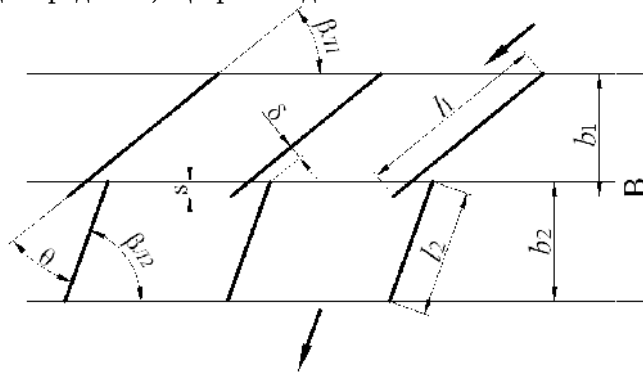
Схема розгортки циліндричного перерізу біпланного шнекового робочого колеса
